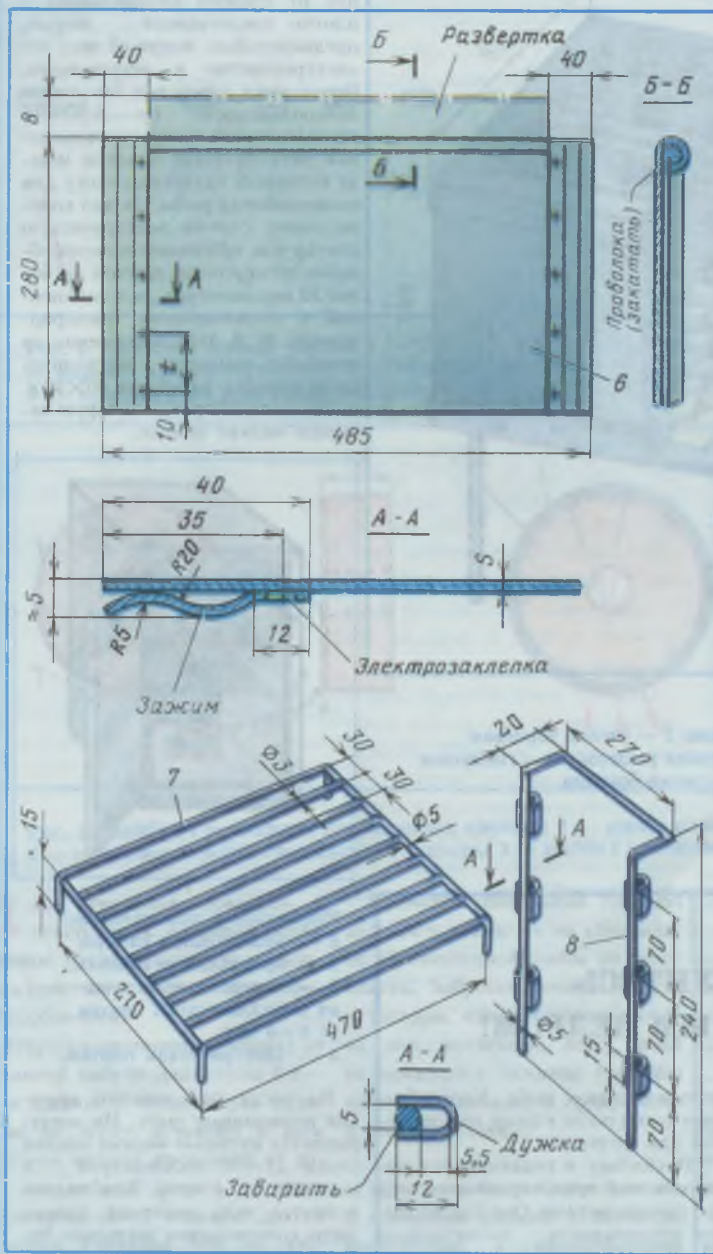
Детали коптильни: 1 — доньшко (крышка);
